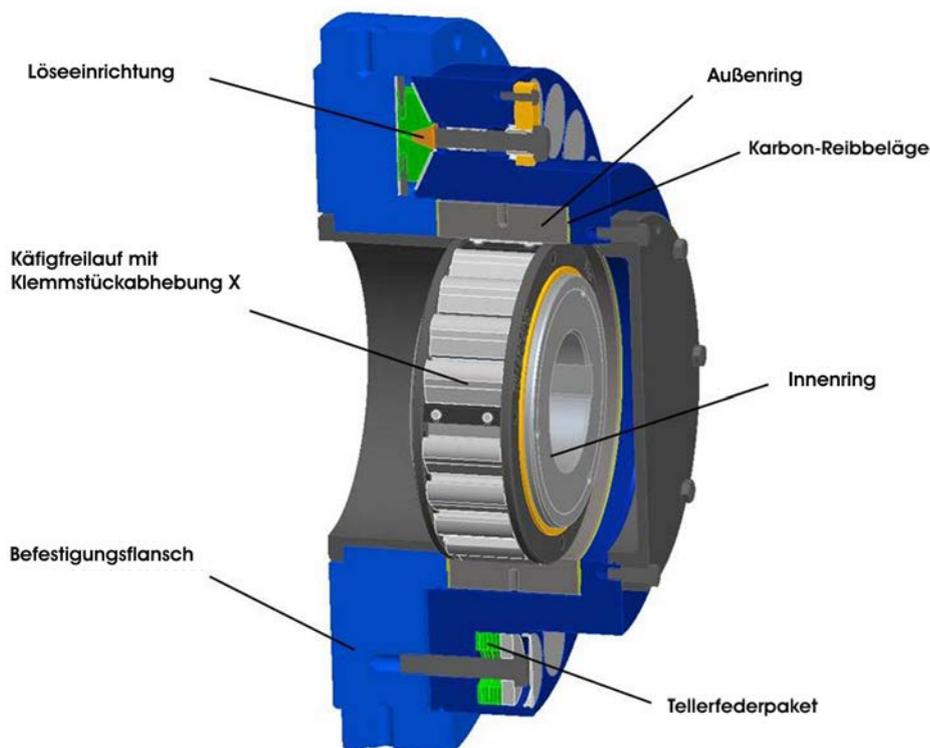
Kompakte Abmessungen: Neuestes Design einer Rücklaufsperrern mit Drehmomentbegrenzung
